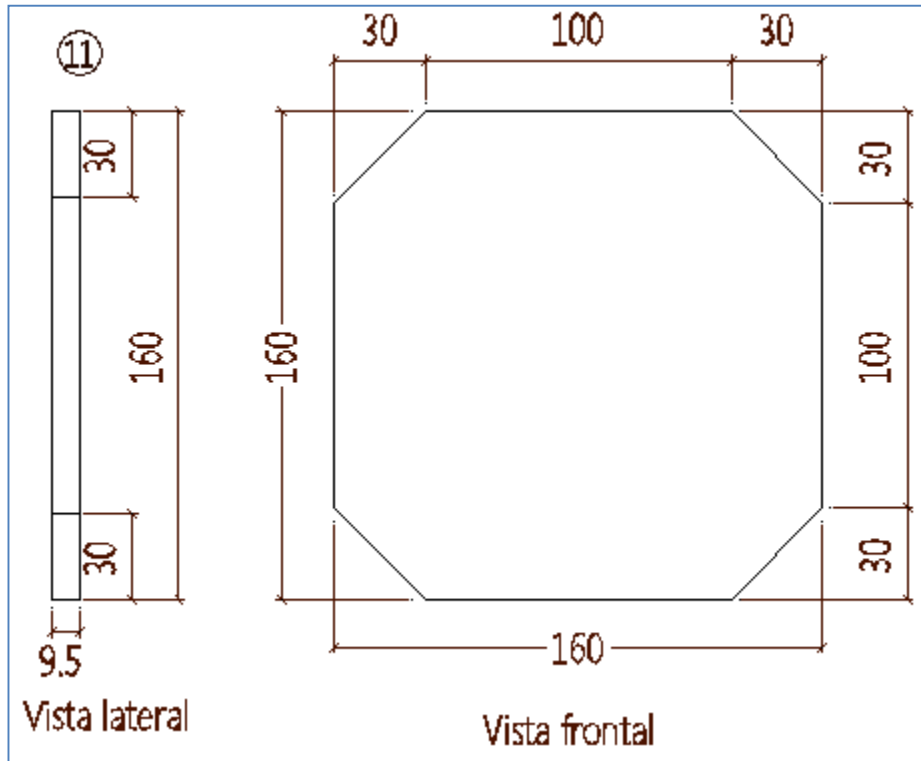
Detalle despiece pieza No.11 modelo 3 tensión.
